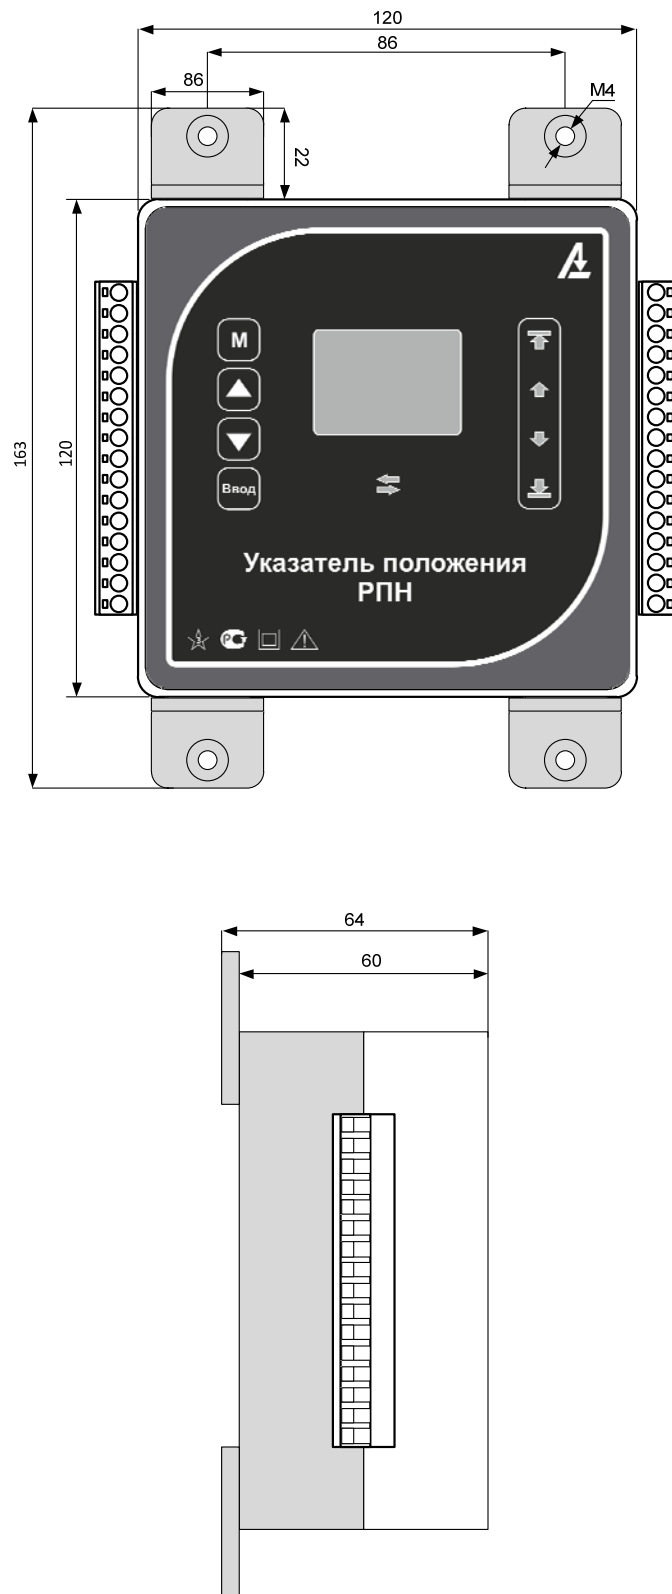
Габаритные размеры щитового варианта указателя положения РПН УП 23-А
